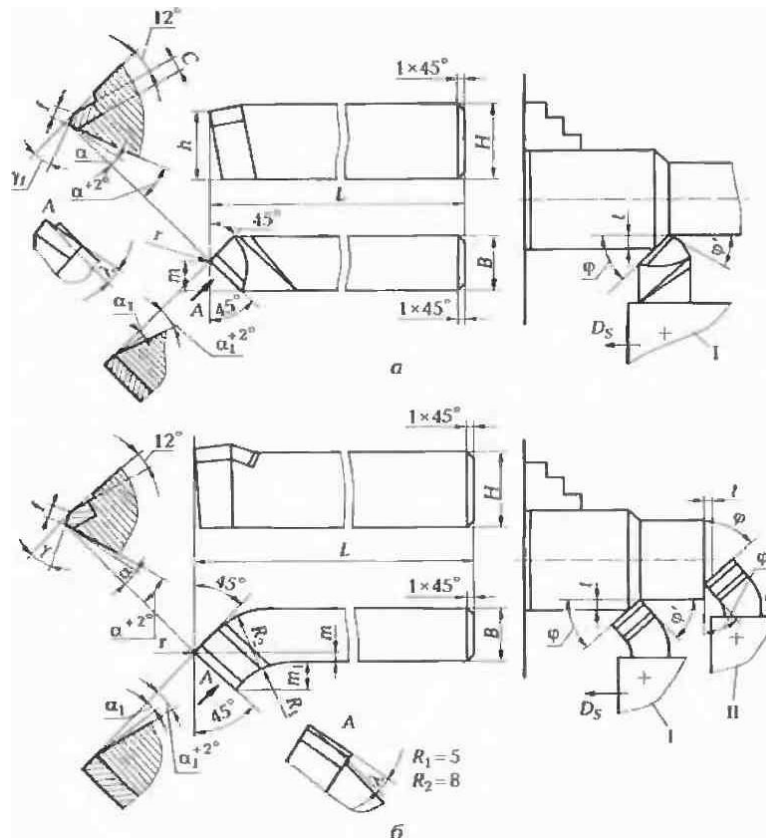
Токарные проходные резцы, оснащенные пластинами из твердого сплава:
